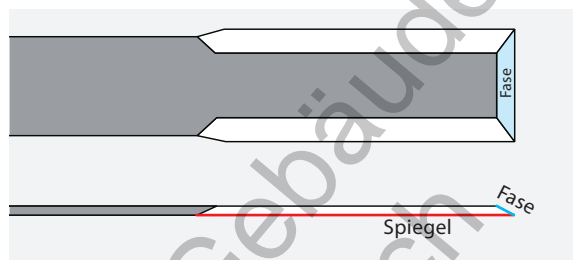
/123: Schnittwerkzeuge, Fase und Spiegel
